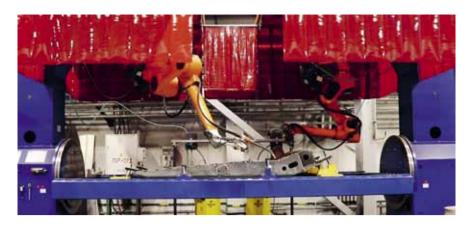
Роботизированный комплекс CLOSS для сварки металлоконструкций
